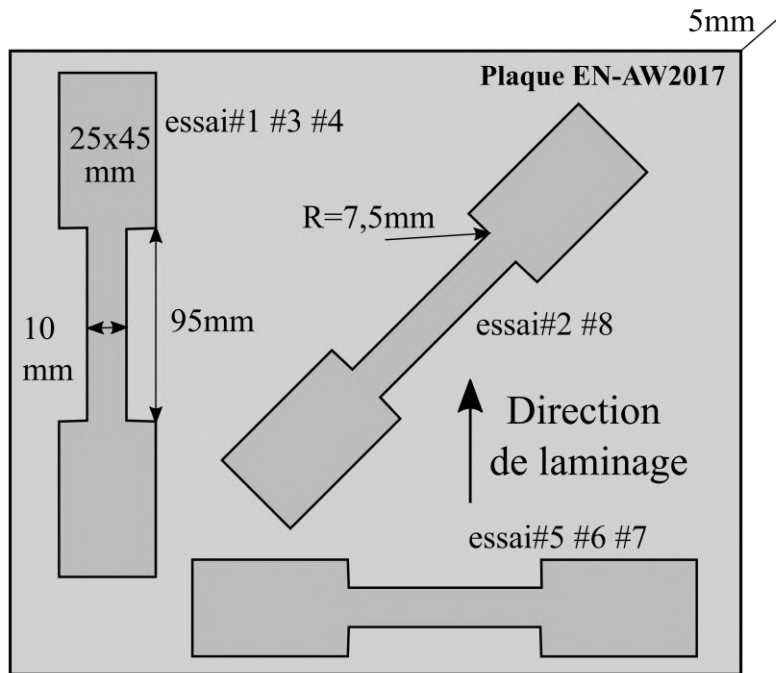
Direction de découpe des éprouvettes pour le matériau EN-AW2017
